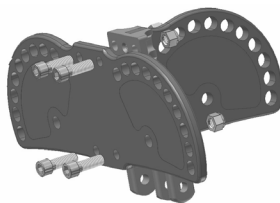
Befestigung einer Halbplatte an Hauptplatte
